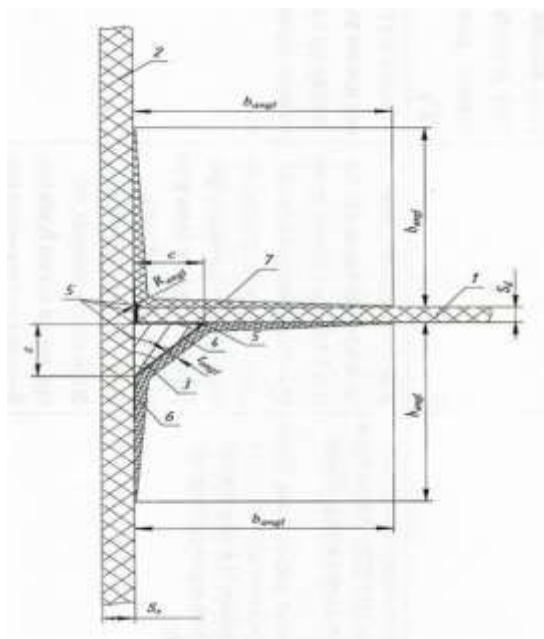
Вузол з'єднання внутрішньої палуби (платформи) з обшивкою борту одношарової конструкції: 1 - настил внутрішньої палуби (платформи); 2 - обшивка борту; 3 - опорний елемент; 4 - обформовка; 5 – адгезійна речовина; 6 - нижній приформовочний косинець; 7 - верхній приформовочний косинець
